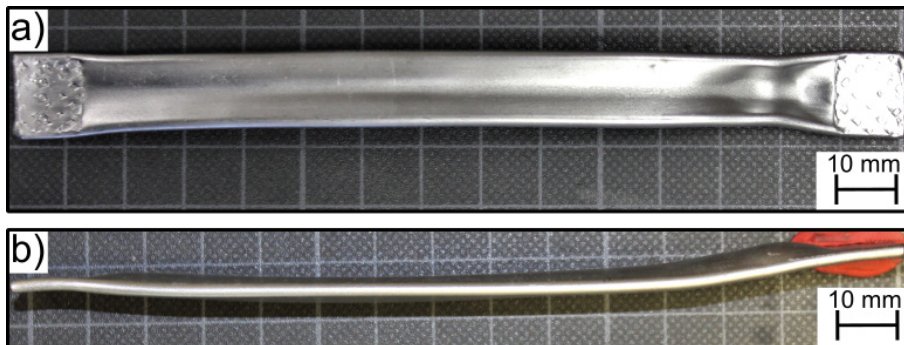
Makroskopische Aufnahme einer HIP-Probe aus Schleifspänen der Fraktion $<45 \mu\text{m}$ mit einer Vorverdichtung der Kapselbefüllung mit einem axialen Pressdruck von 100 N. a) zeigt die Draufsicht auf die HIP-Kapsel, b) die Seitenansicht der HIP-Kapsel.
